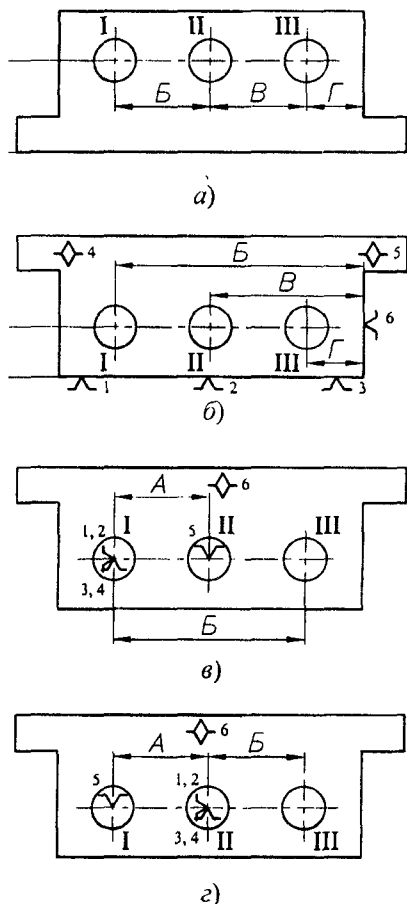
Варианты базирования заготовки корпусной детали на первой операции:
